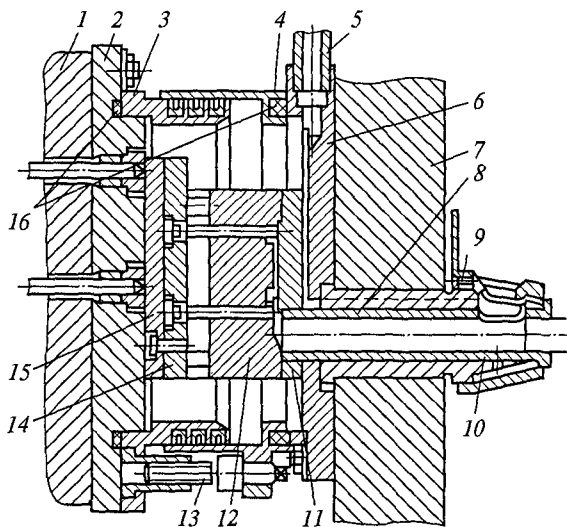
Установка для литья под давлением с вакуумированием пресс-формы:
